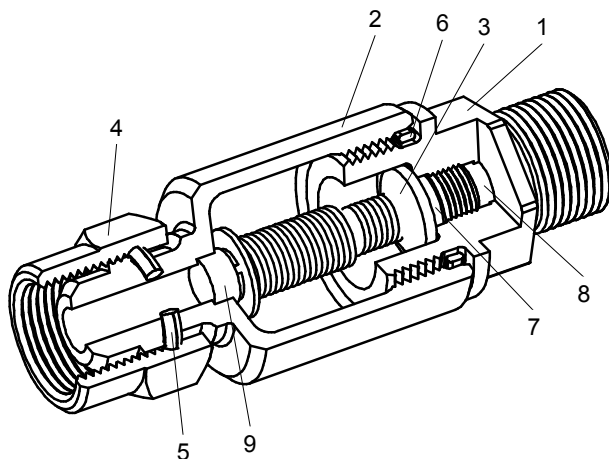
Устройство гасителя колебаний давления: 1 – корпус; 2 – крышка; 3 – дросселирующая вставка; 4 – накидная гайка; 5 – стопорное кольцо; 6, 7 – резиновое уплотнительное кольцо; 8, 9 – фильтры
